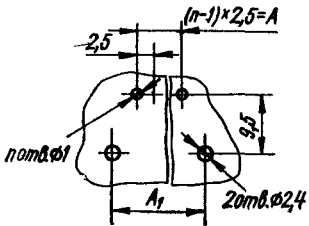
Конструктивные размеры плат ПСП9 и ПСП10 и разметка для их крепления:
